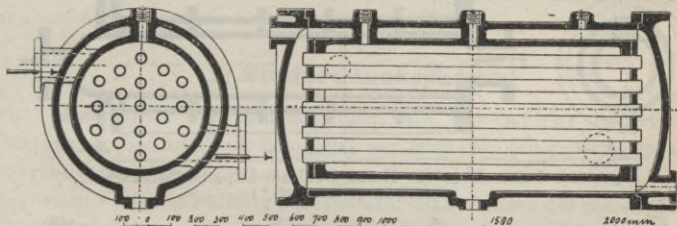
1656. Receiver für stehende Wasserwerksmaschine.
